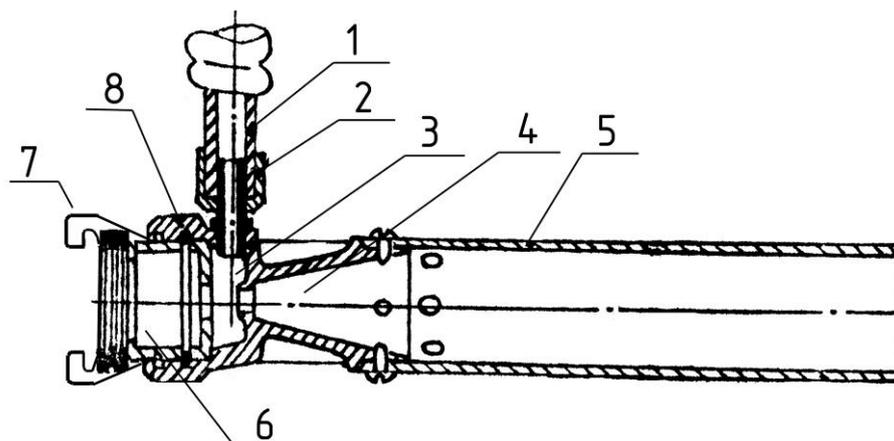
Ствол воздушно-пенный с эжектирующим устройством типа СВПЭ (1 – шланг; 2 – ниппель; 3 – вакуумная камера; 4 – выходная камера; 5 – направляющая труба; 6 – приемная камера; 7 – соединительная головка; 8 – корпус)
